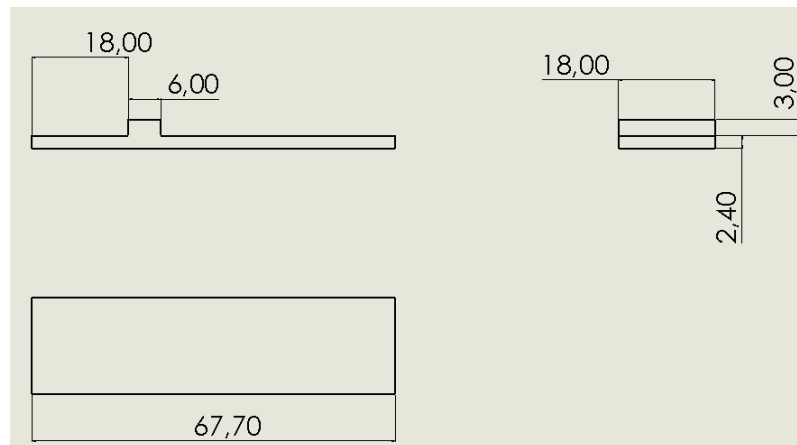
Medidas de la base para soporte ball and beam. Autoría propia
